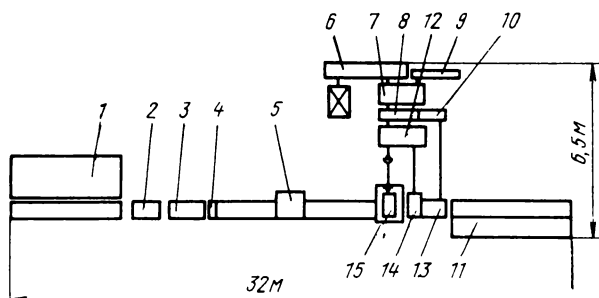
Двухниточный стан 2 ХПТС 8-25:
